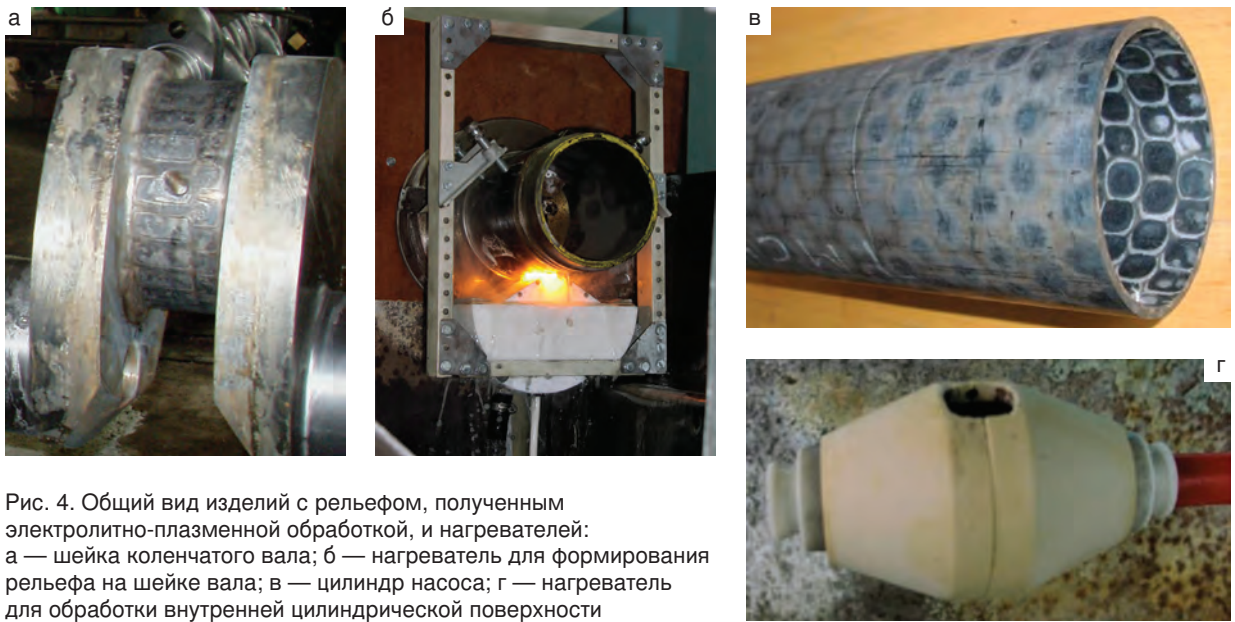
Общий вид изделий с рельефом, полученным электролитно-плазменной обработкой, и нагревателей: а — шейка коленчатого вала; б — нагреватель для формирования рельефа на шейке вала; в — цилиндр насоса; г — нагреватель для обработки внутренней цилиндрической поверхности
